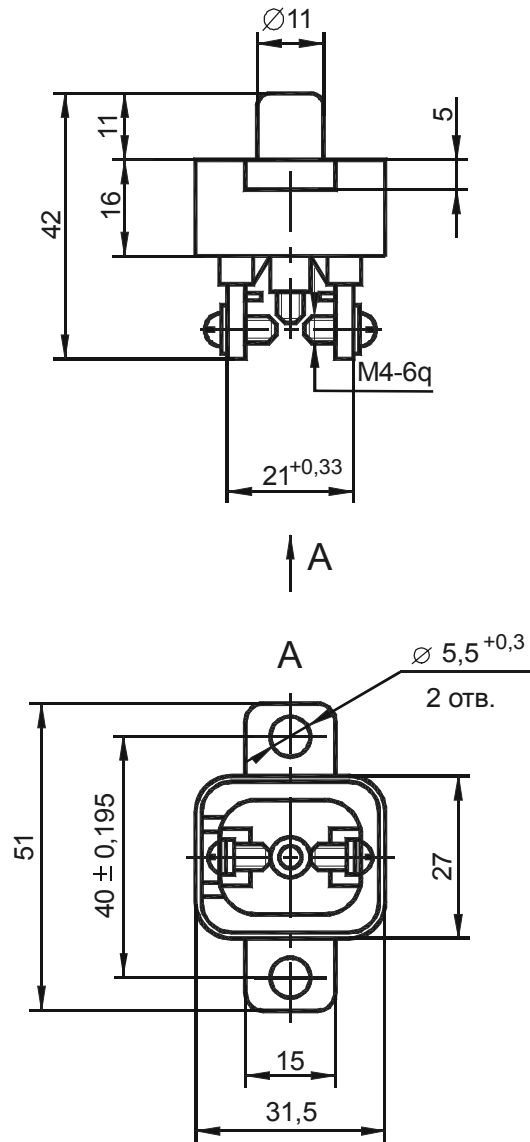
Предохранитель терробиметаллический 29.3722.
